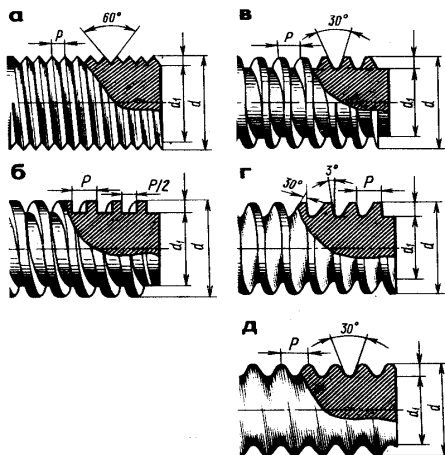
Профили и элементы резьбы: P – шаг резьбы; φ – угол профиля (60° , 30°); t – высота профиля ($t = d - d_1$); d_1 – внутренний диаметр; d – наружный диаметр
